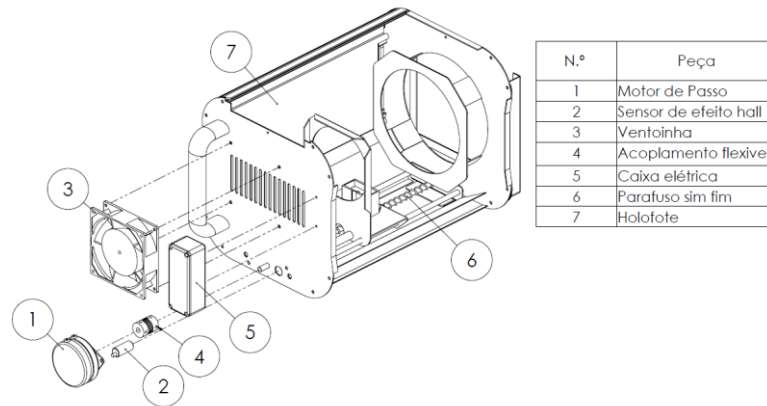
Posição do motor, sensor de efeito Hall e sistema de arrefecimento.
